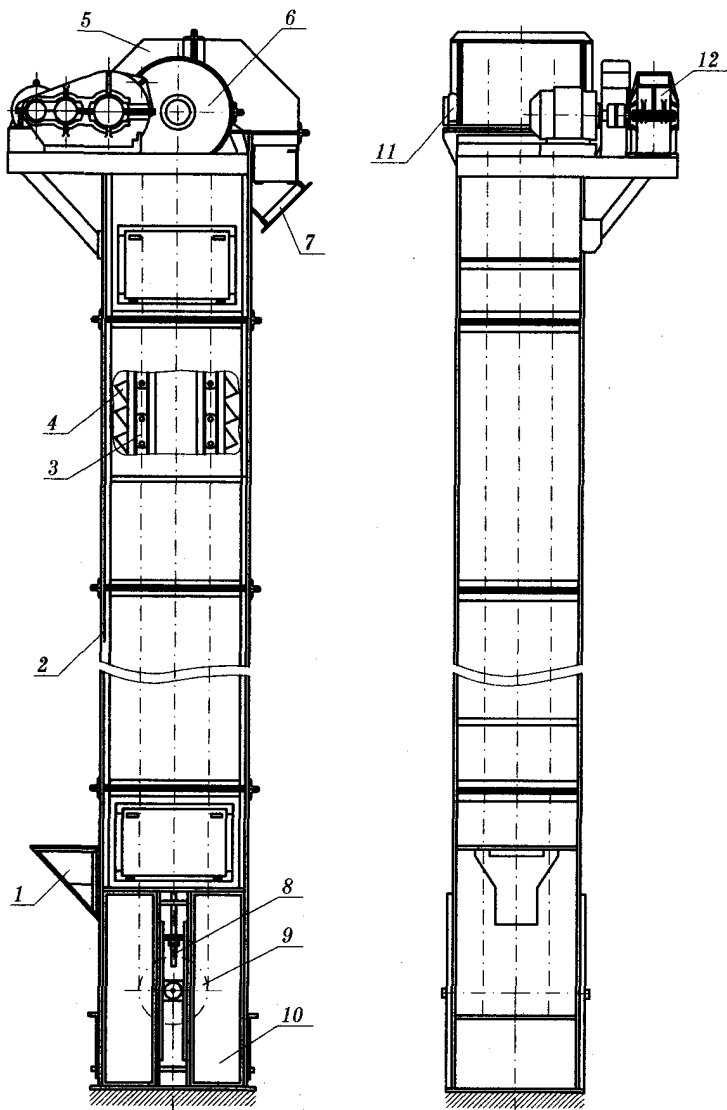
Ківшовий елеватор: 1, 7 – завантажувальний і розвантажувальний патрубкі; 2 – кожух; 3 – тяговий елемент; 4 – ківш; 5 – верхня частина (головка); 6, 9 – привідний і натяжний барабани (або зірочки); 8 – натяжний пристрій; 10 – нижня частина (башмак); 11 – зупинник; 12 – привід
